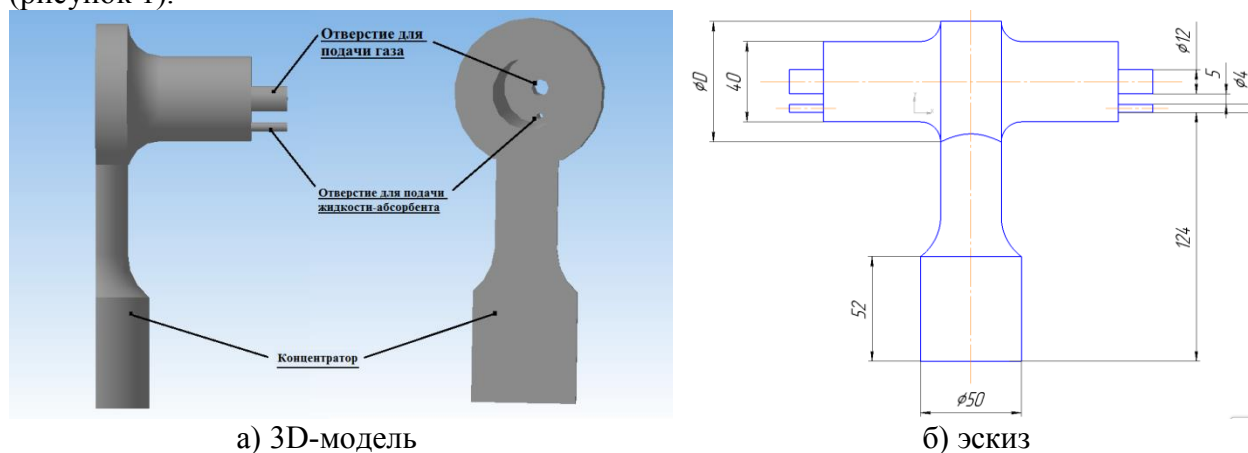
Излучатель с трубчатым рабочим инструментом
